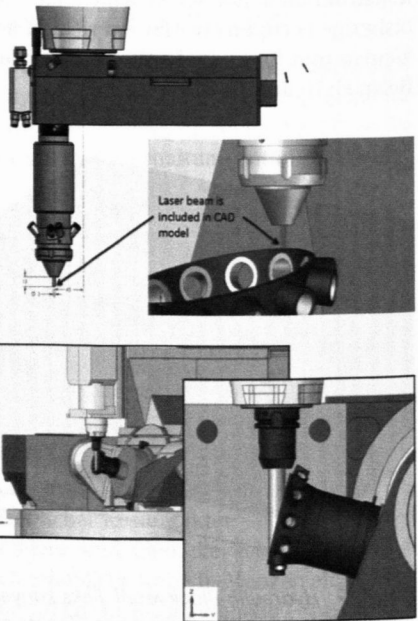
3D Modell – Material-Auftrag (AM) und Abtrag (Fräsen) auf einer Maschine (Quelle: DMG-Mori)
